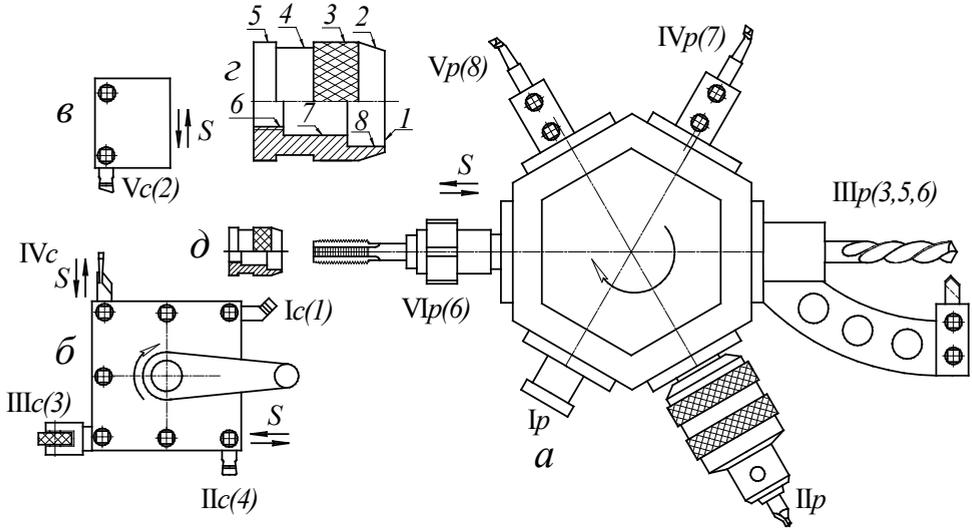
Наладка ТРС на комплексную деталь для обработки деталей группы
